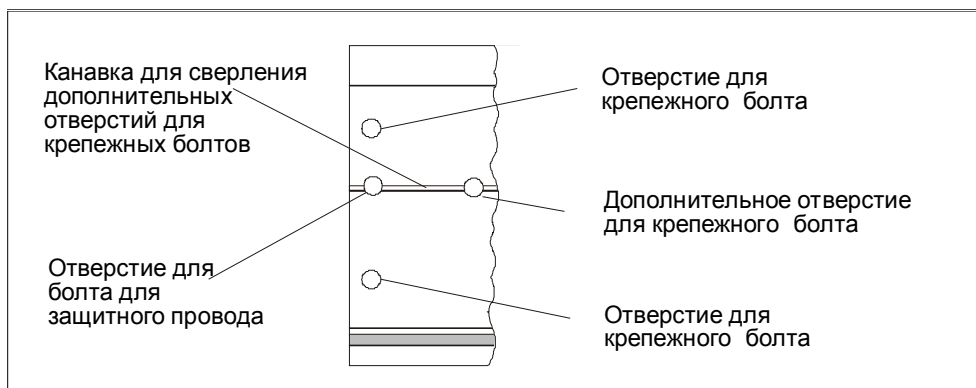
Крепежные отверстия для 2-метровой профильной шины
